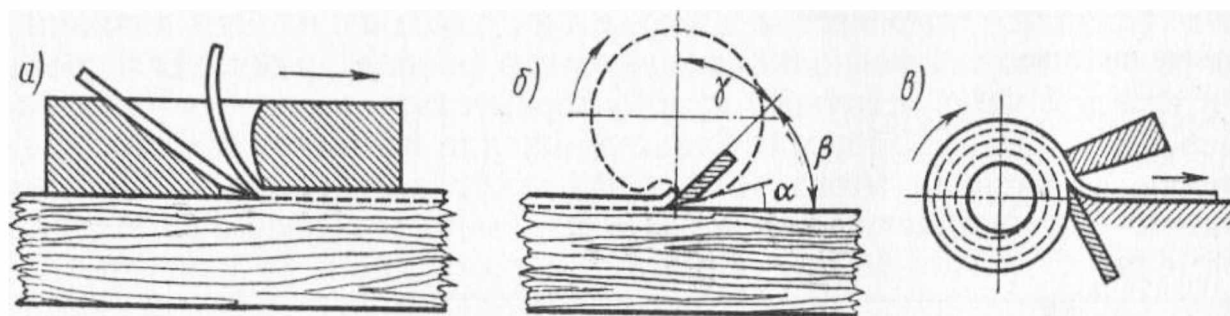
Схеми обробки деревини: а - стругання; б - фрезерування;
